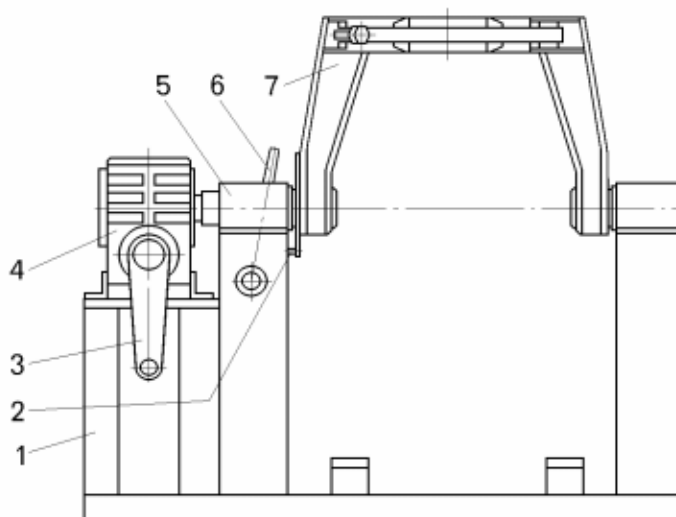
Стенд для разборки и сборки цилиндров пневмогидравлической подвески:
